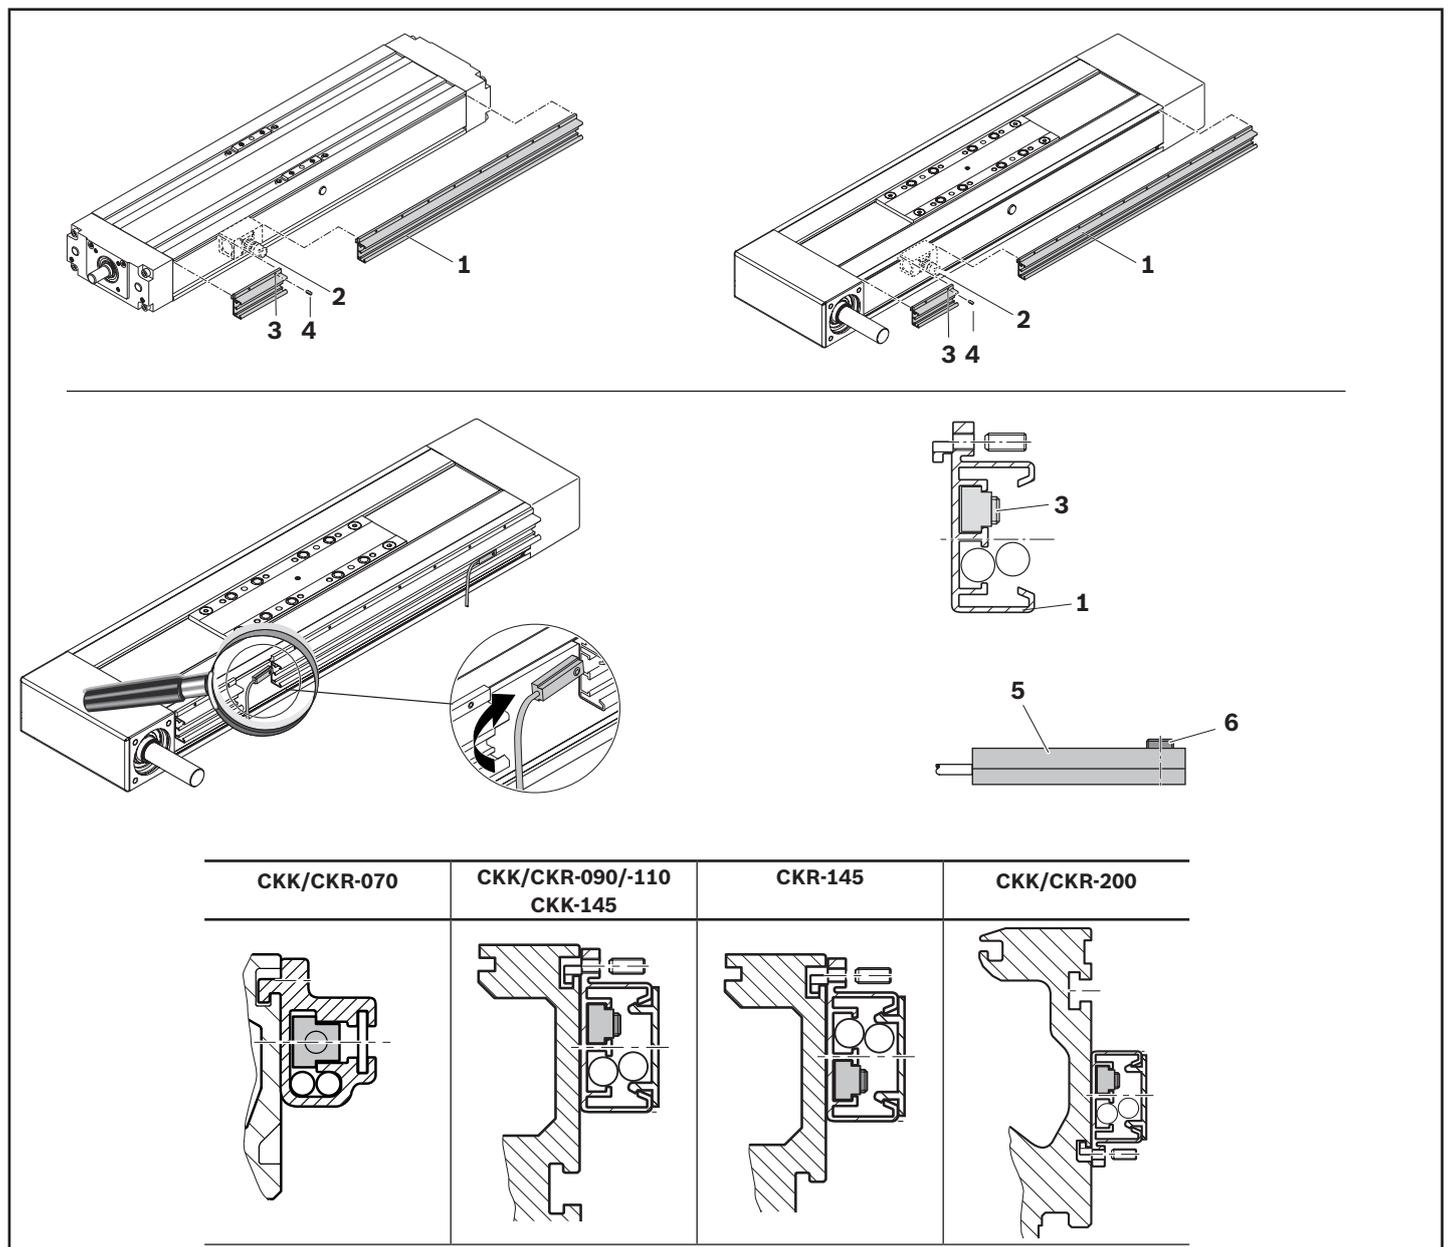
Befestigungskanal/Magnetischer Sensor montieren
